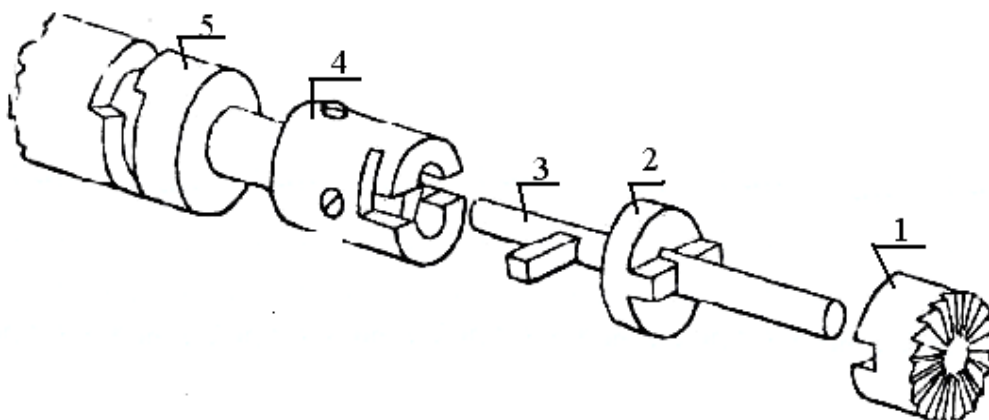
Эскиз конструкции насадной цековки (Тульский завод, 1826 г.)
